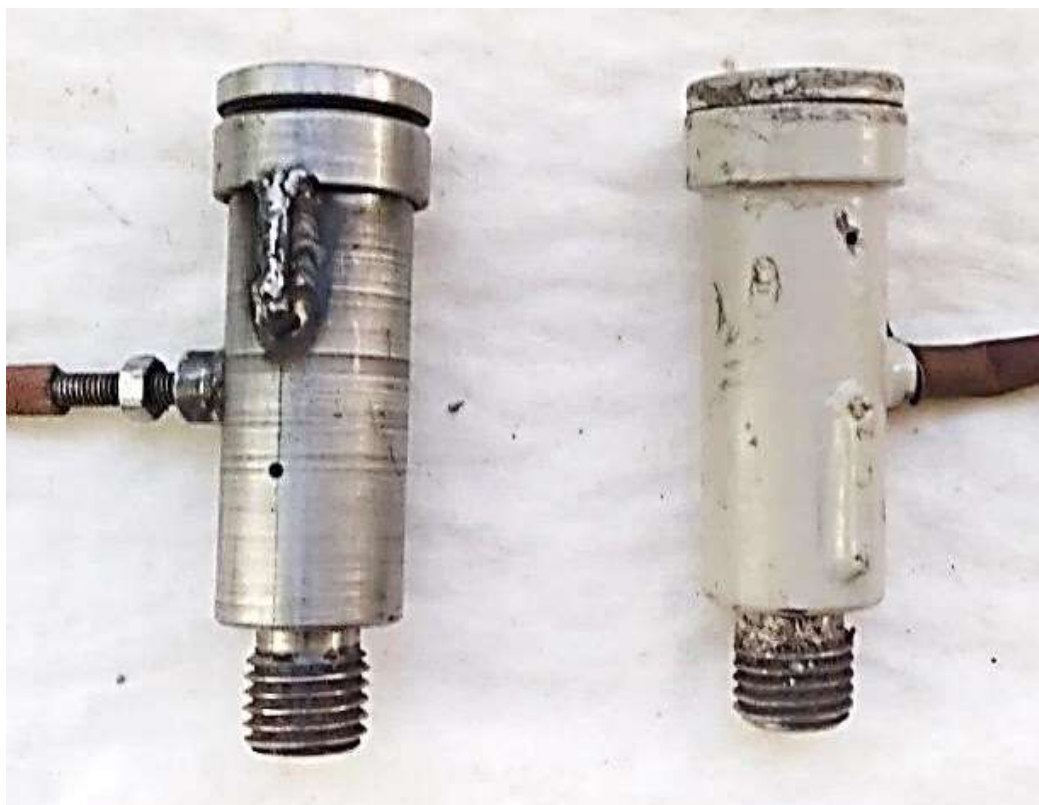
Изготовленный комплект пневматических вибраторов поршневого типа для модернизированного манипулятора
